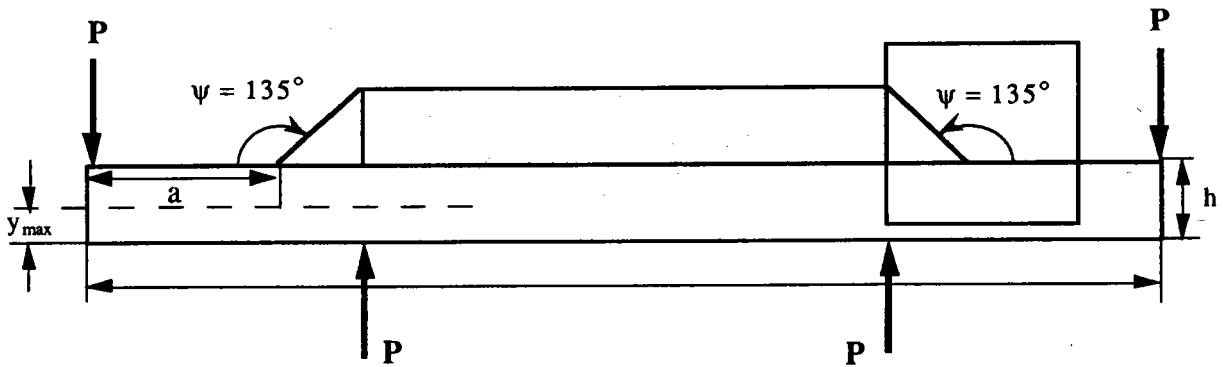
Une éprouvette simulant un joint soudé
